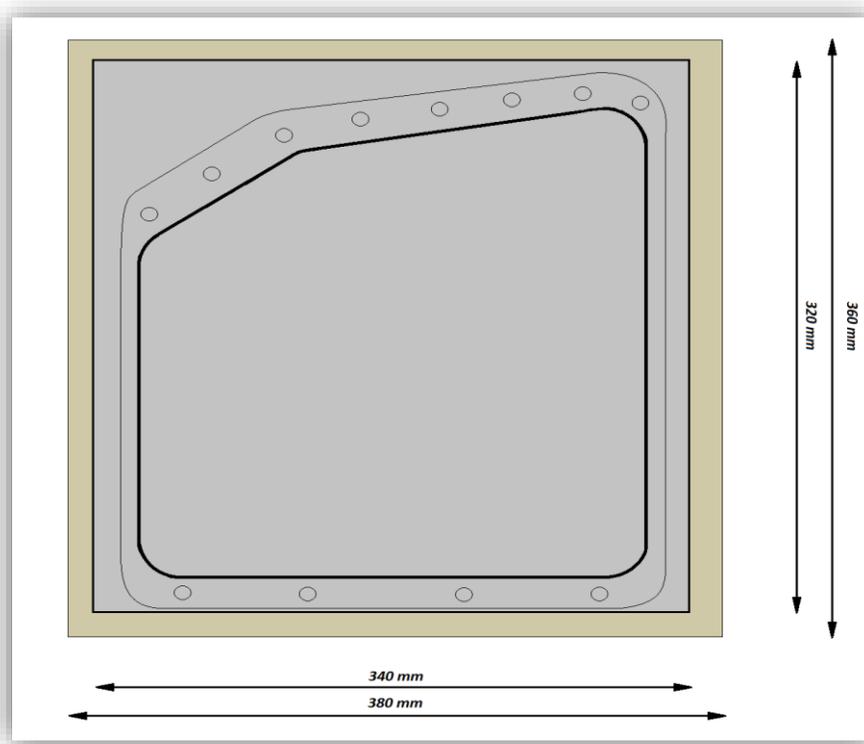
Dimensiones principales del inserto para las dos versiones de fabricación. *Fuente: Elaboración Propia
